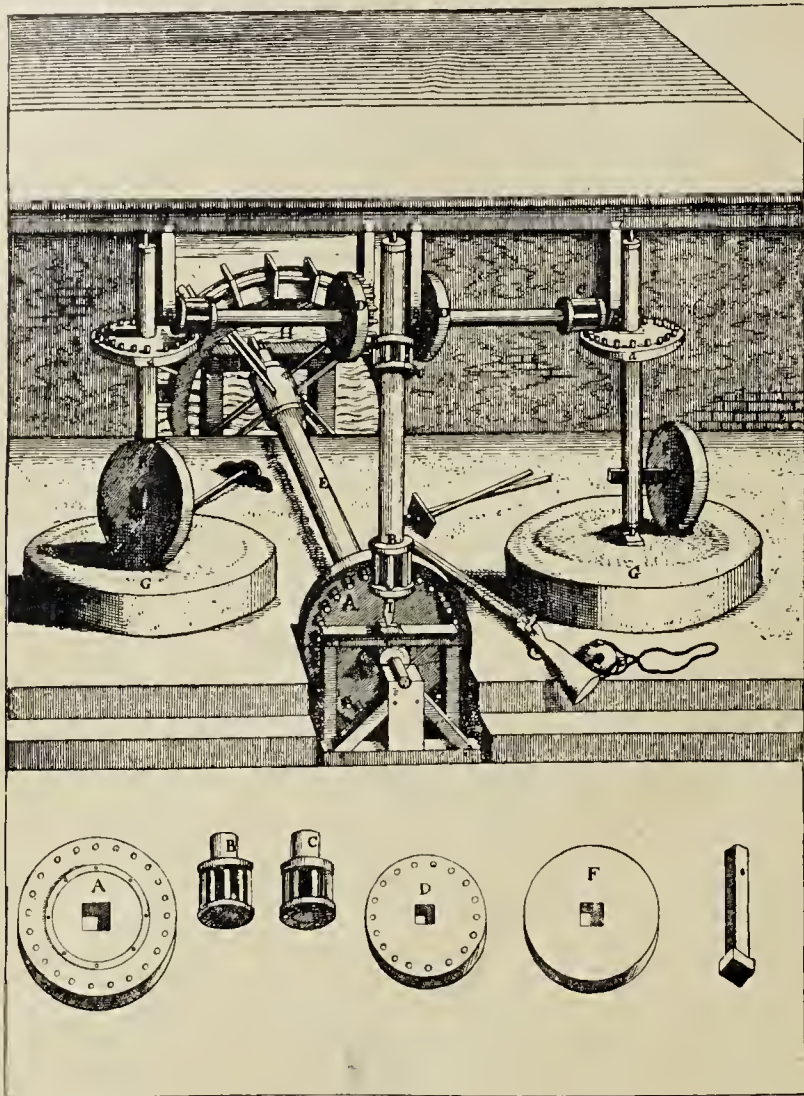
Pulvermühle mit zwei Kollergängen und Wasserantrieb.
